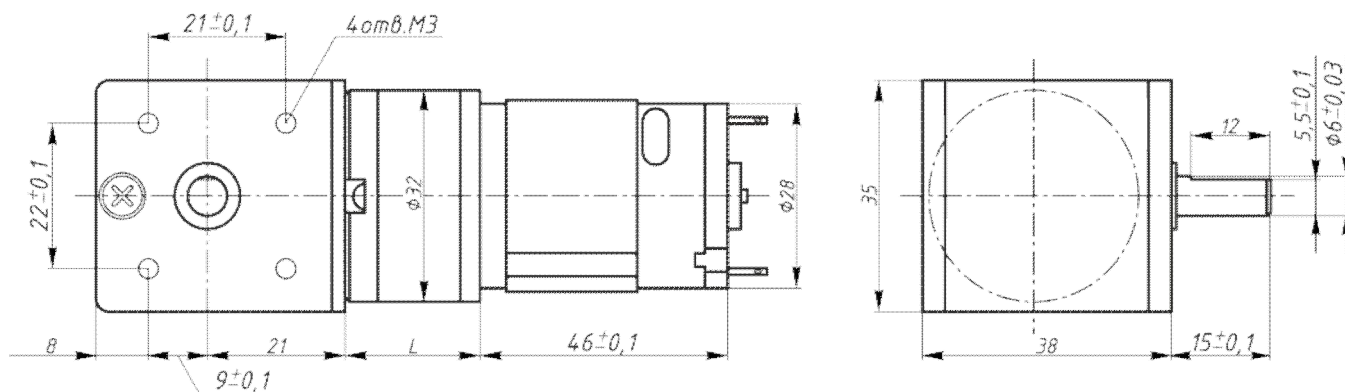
Габаритні і приєднувальні розміри мотор-редуктора IG-32RGM
